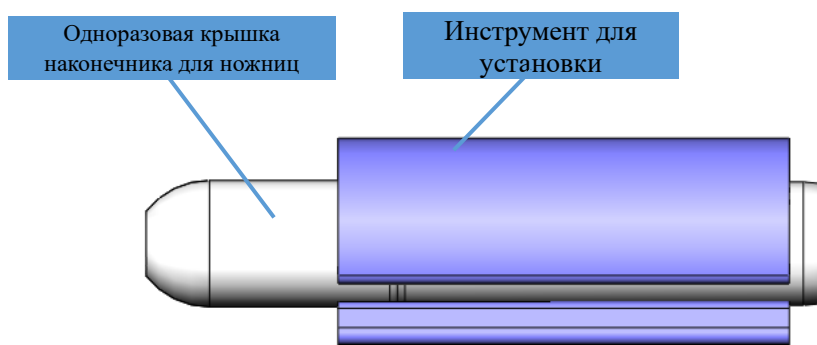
Схематическое изображение конструкции принадлежности крышки наконечника ножниц одноразового использования
